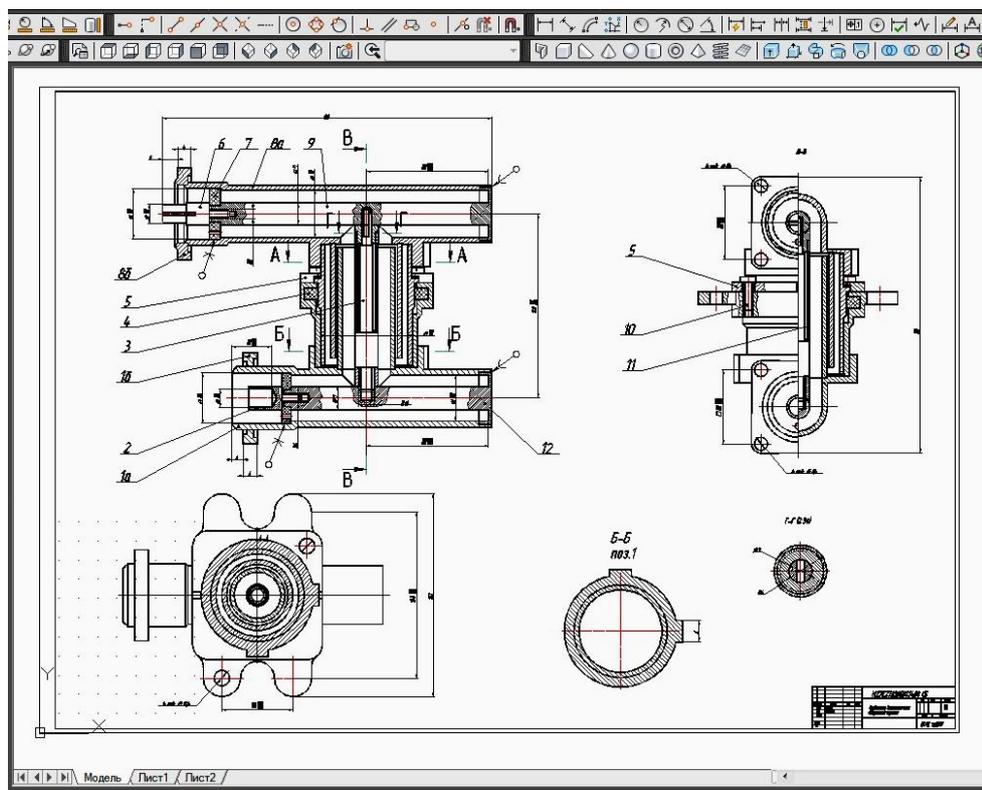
Сборочный чертеж, выполненный с использованием растрового изображения в качестве базового.
